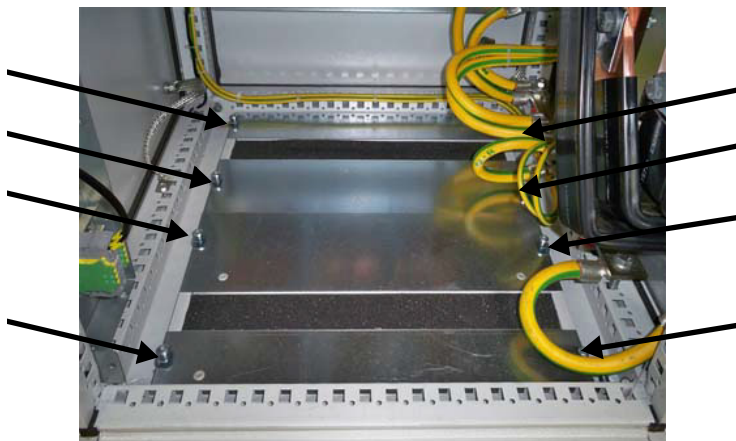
Rimozione della piastra sul fondo dell'armadio CA
